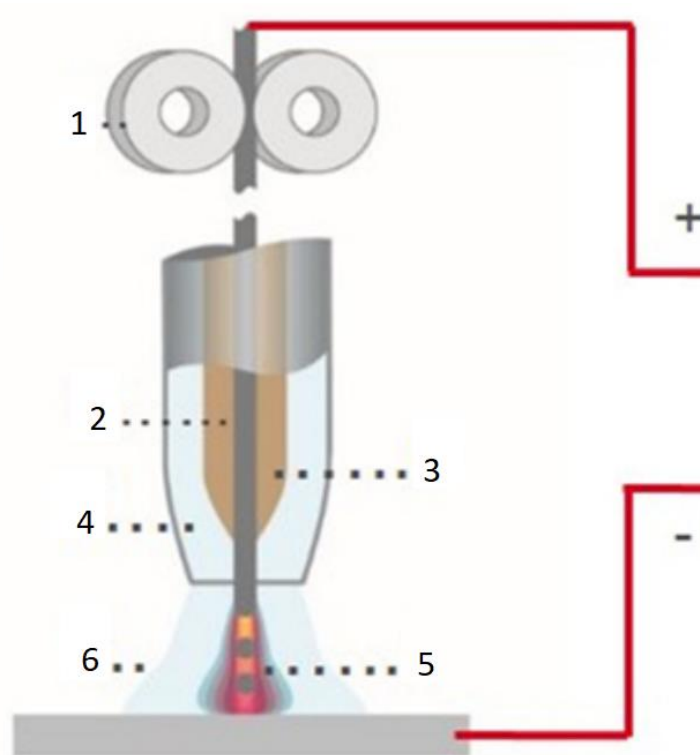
Принципова схема процесу MIG/MAG зварювання
